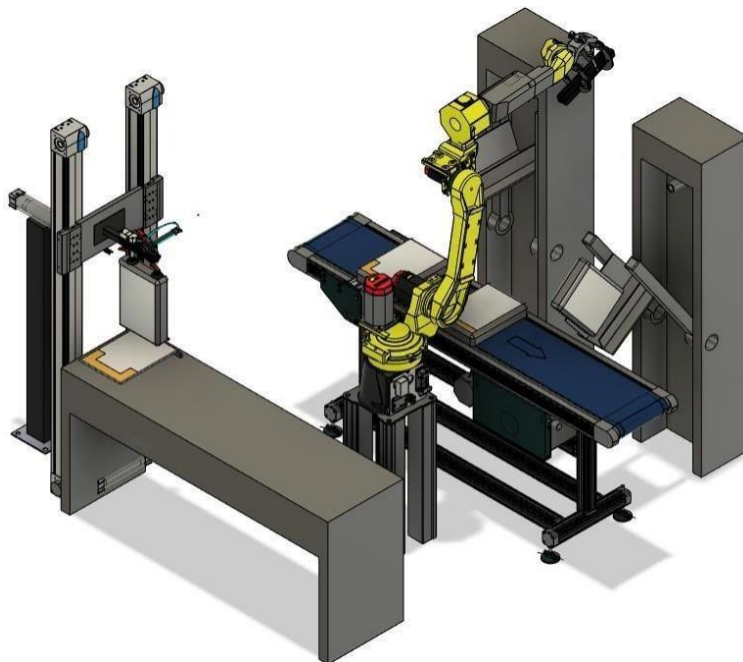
Підняття мішку завдяки пневматичного захвату
